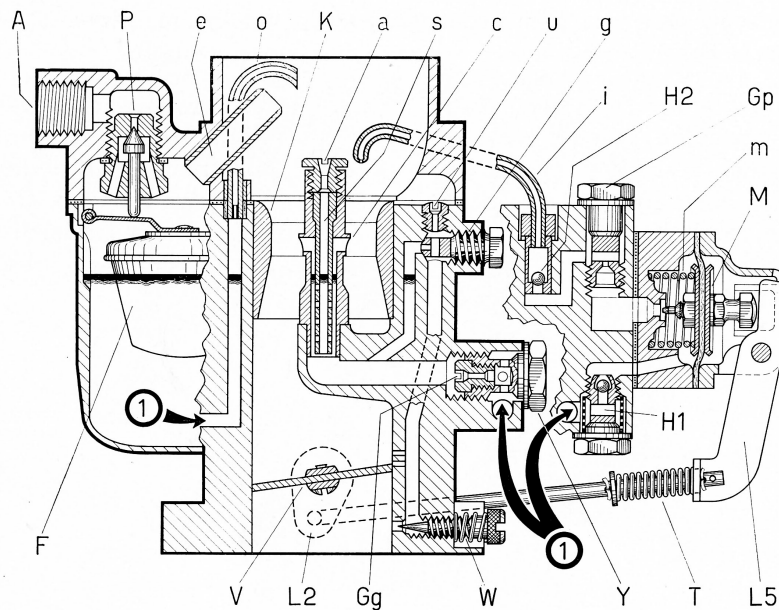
SOLEX-Vergaser Type 32 PICB - 1
